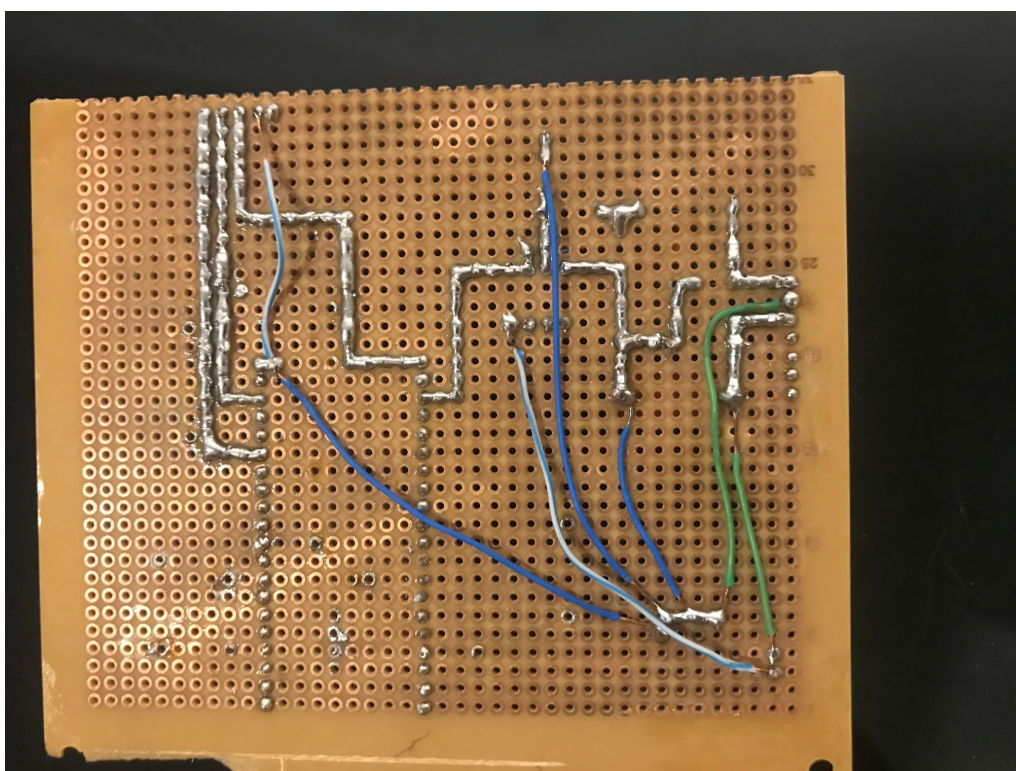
Placa de circuito impresso com o produto final (lado traseiro das soldaduras)
